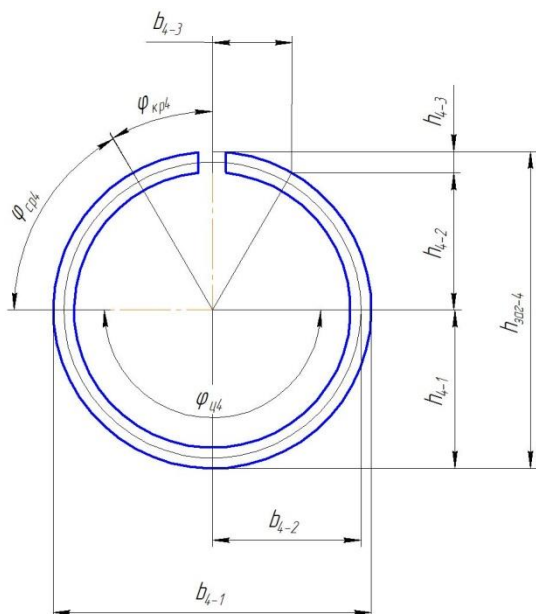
Геометрические параметры O – образного профиля трубной заготовки
